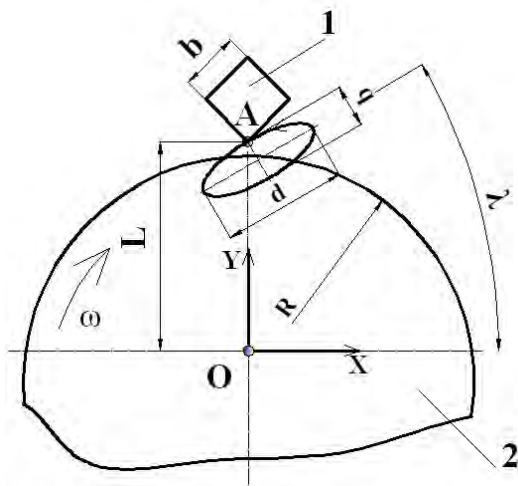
Схема для математического описания движения точки на поверхности заготовки, совершающей эллиптическое движение относительно распиловочного диска:
